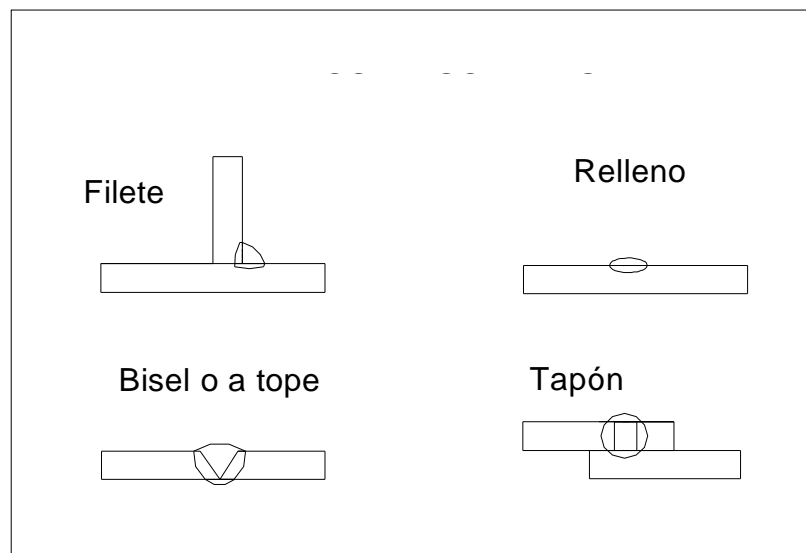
Tipos de soldadura, según perfil soldado (Manual indura_ soldadura, Pág. 15).
